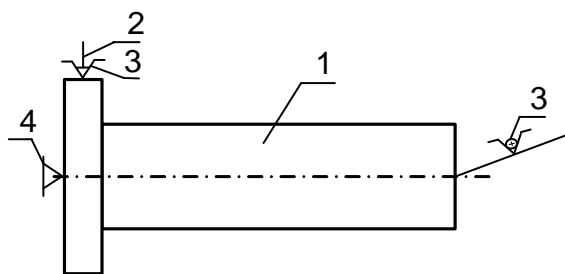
Графическое изображение крепления заготовки в установе:
